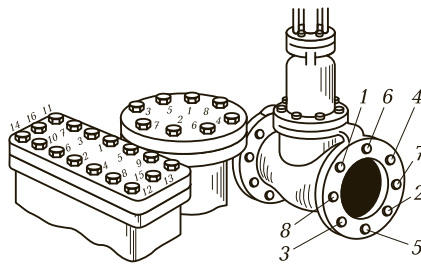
Порядок затягивания резьбовых соединений (указан цифрами 1–16)
